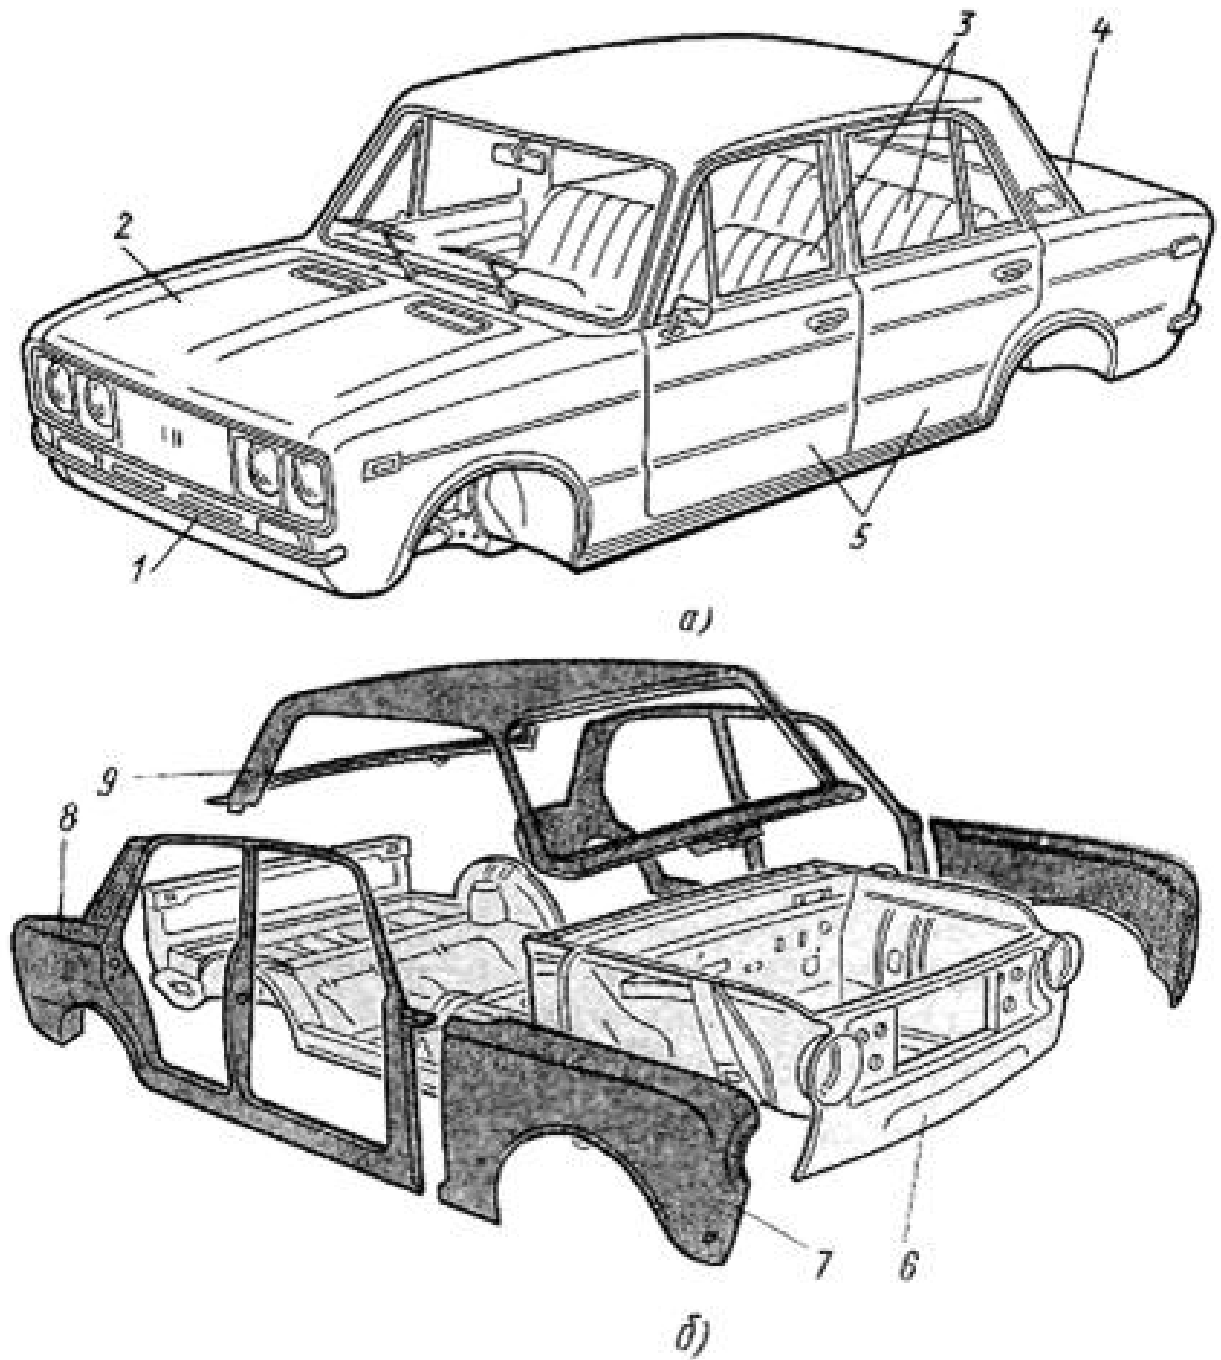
Кузов легкового автомобиля "Жигули": а – в сборе модель ВАЗ-2106; б – корпус модели ВАЗ-2101
